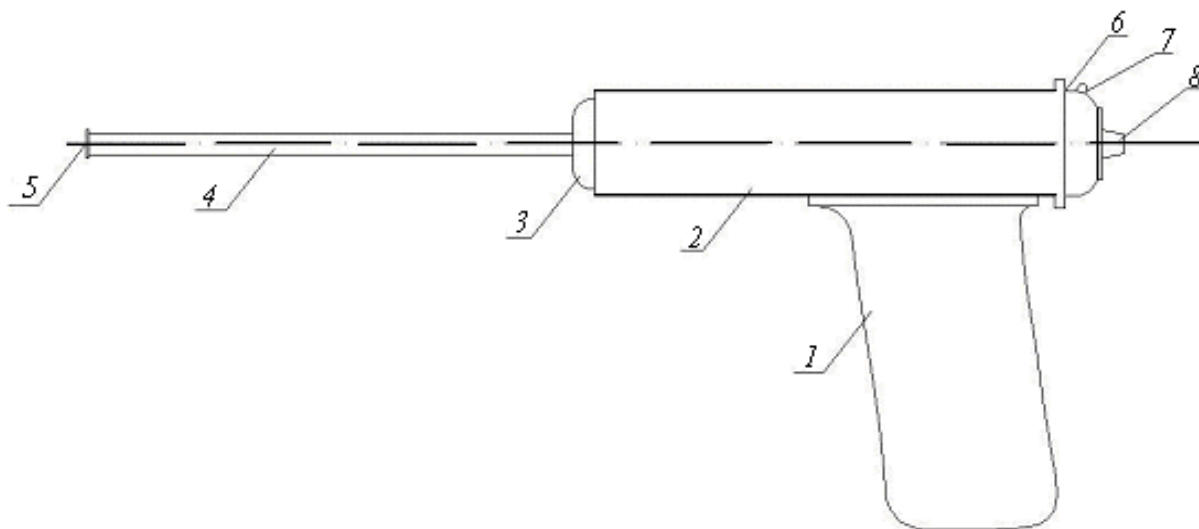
Электронный акустический течеискатель: 1 – рукоятка; 2 – цилиндрический корпус; 3 – крышка корпуса; 4 – цилиндрический щуп; 5 – датчик; 6 – задняя крышка; 7 – светодиод; 8 – выключатель
